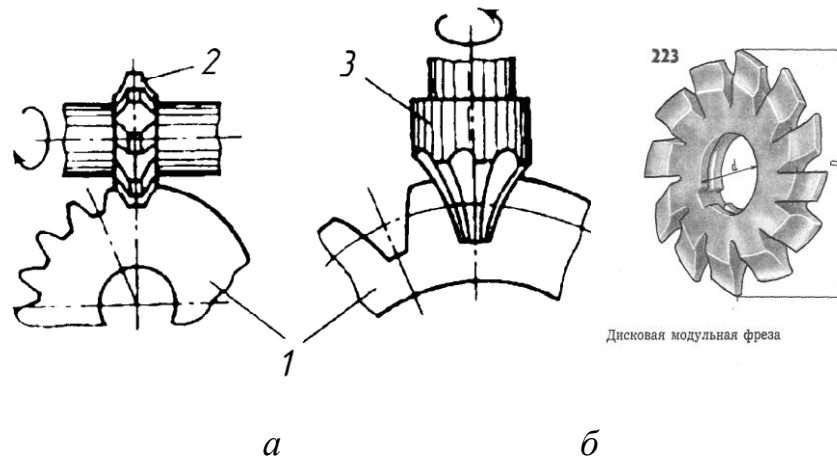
Нарезание зубьев зубчатых колес по методу копирования фрезерованием:
